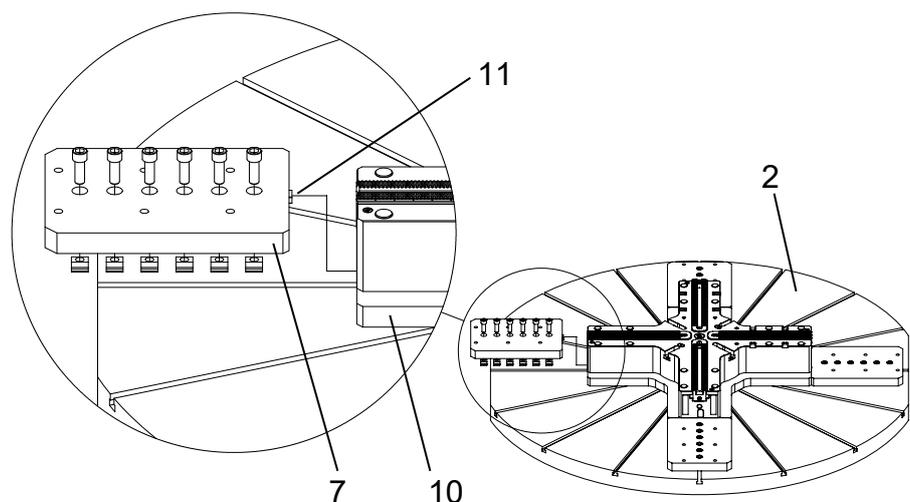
Montage des Grundplatten-Verlängerungen
